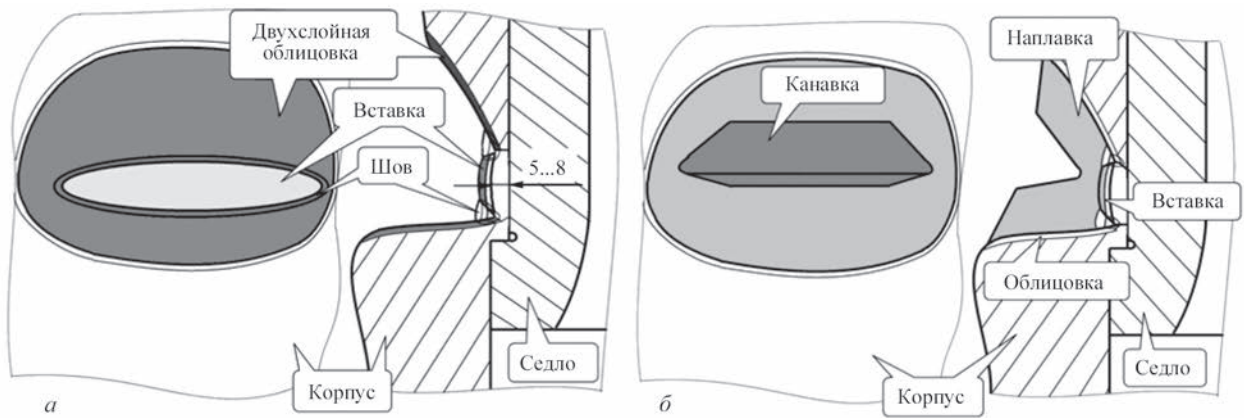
Разделка под сварку трещины в корпусе регулирующего клапана ЦСД и этапы ее заварки
